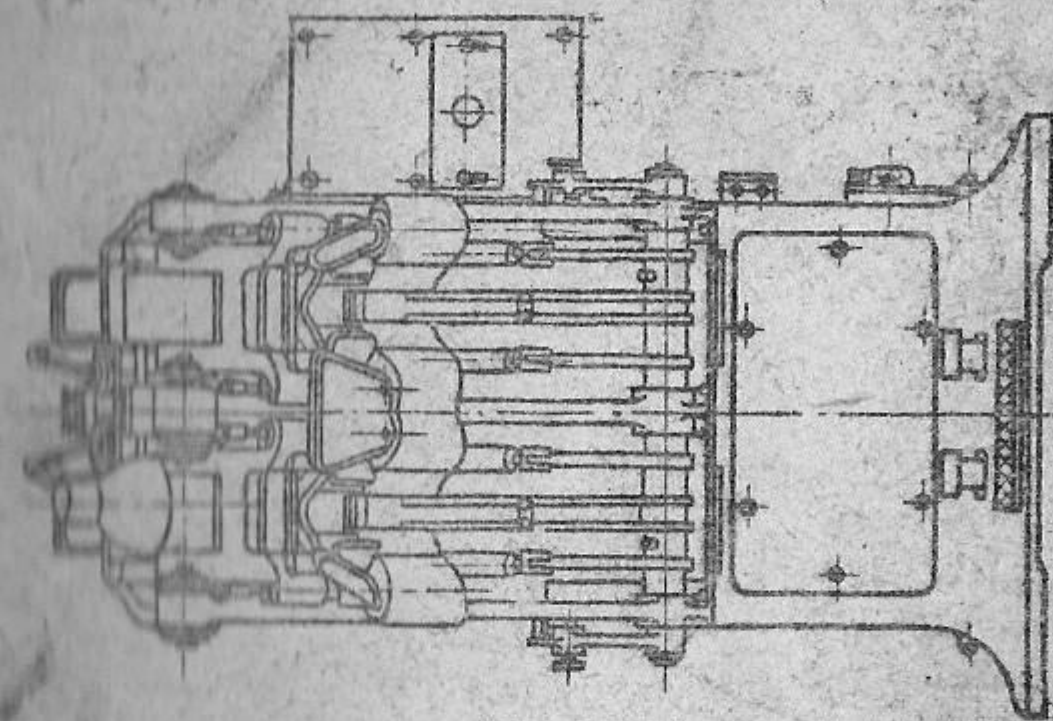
Внешний вид машины ПИТ-1 для предварительного формирования пятачной части заготовки титановой обухи
